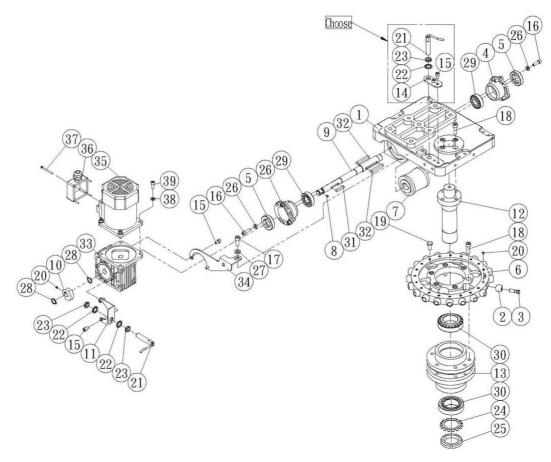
Werkzeugwechsler 4-4 -Tool changer 4-4
